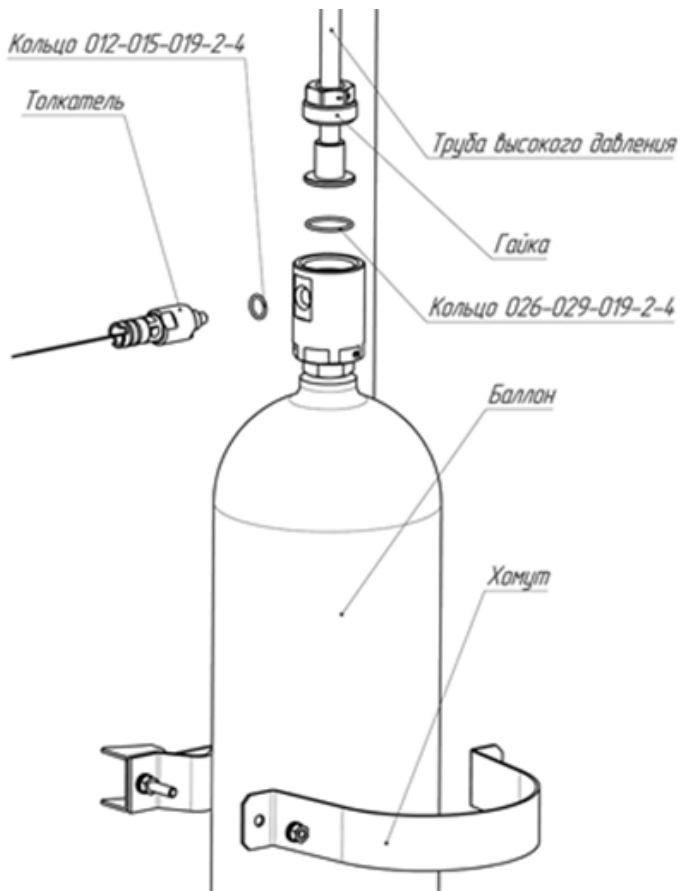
Внешний вид блока рабочего газа «БРГ-10».
